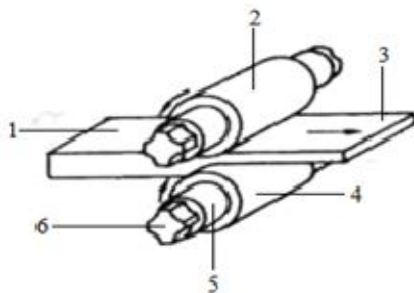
Схема продольной прокатки металла: 1– прокатываемая заготовка, 2 – верхний валок, 3 – направление прокатки, 4 – нижний валок, 5 – шейка валка, 6 – трещина валка
